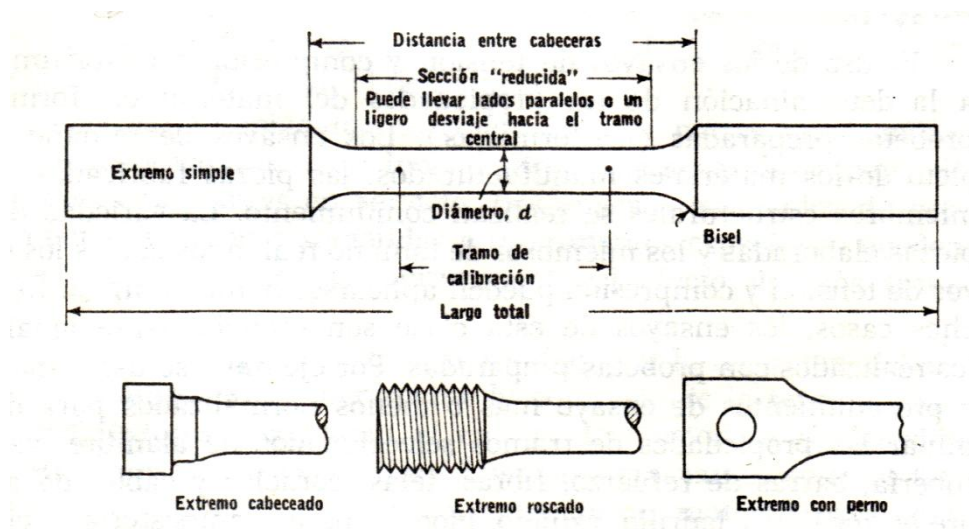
Probeta cilíndrica espécimen 1 para el ensayo de tracción.
